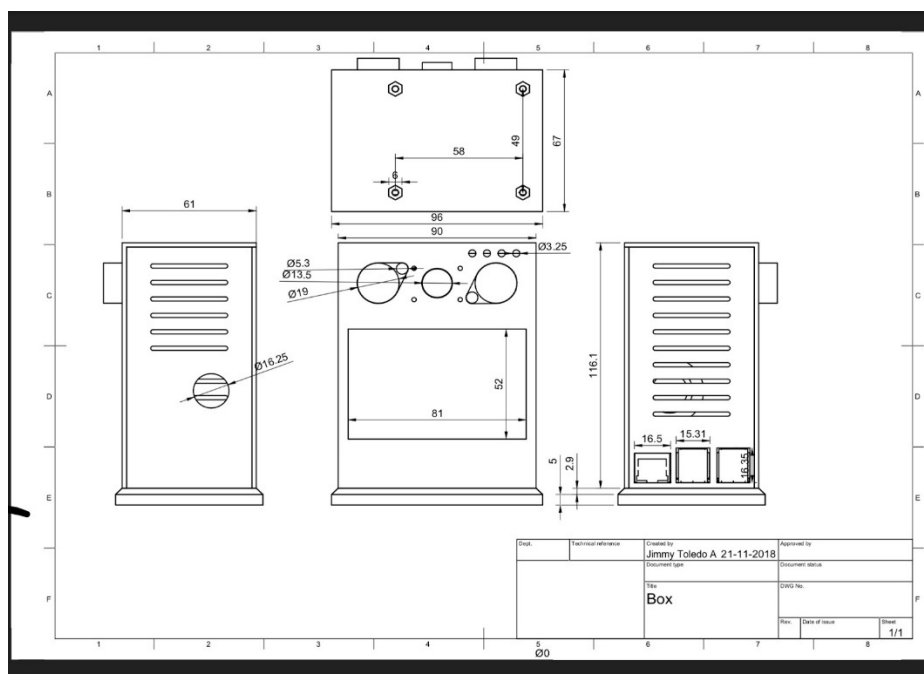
Esquemático y Render de la manufactura del empaquetado. Elaboración propia.
